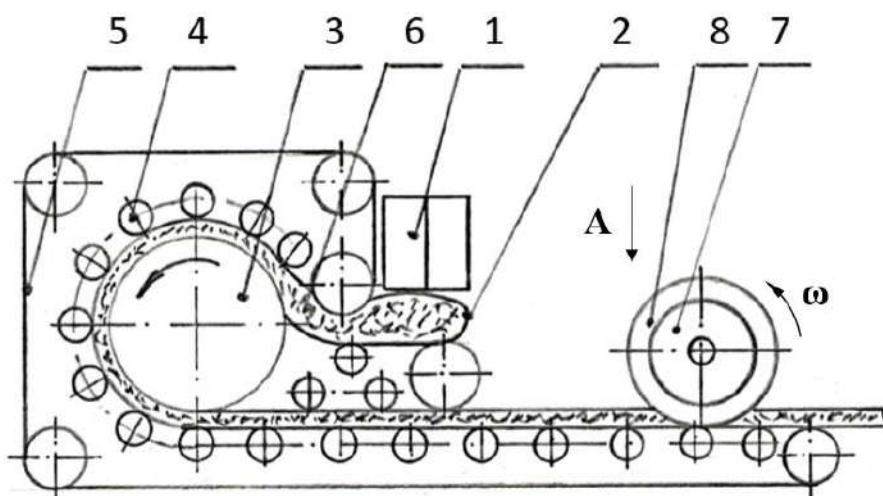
Схема проходного пресса для изготовления погонажных изделий из ДКМ
